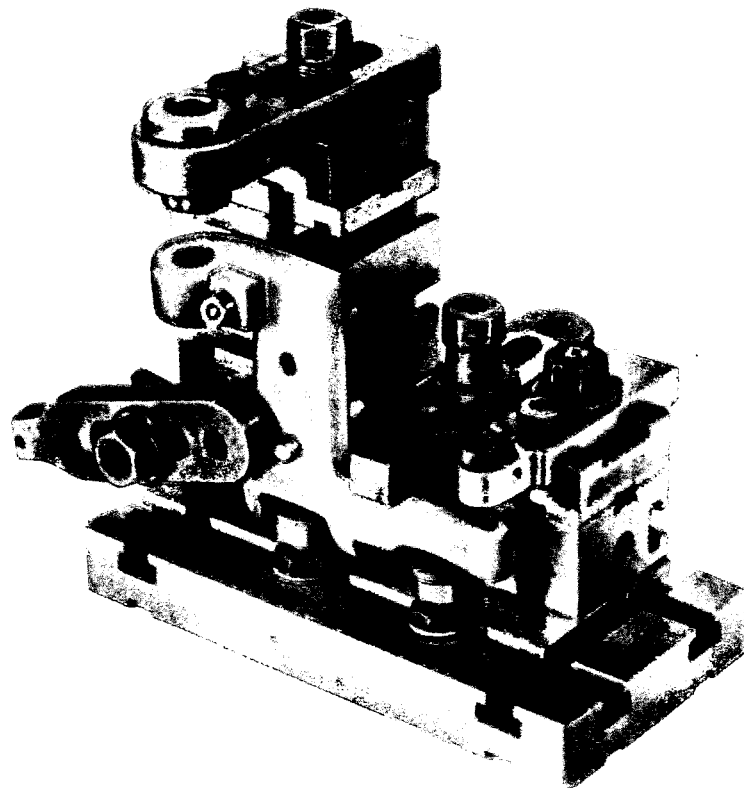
Приспособление для сверления двух отверстий в рычаге
